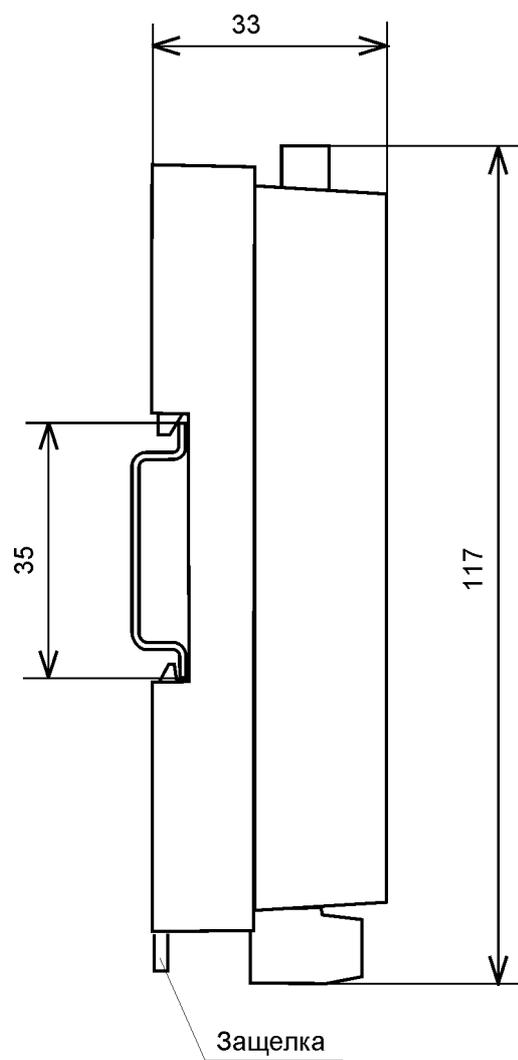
Габаритный чертеж модуля с креплением к DIN-рейке. Вид сбоку.
